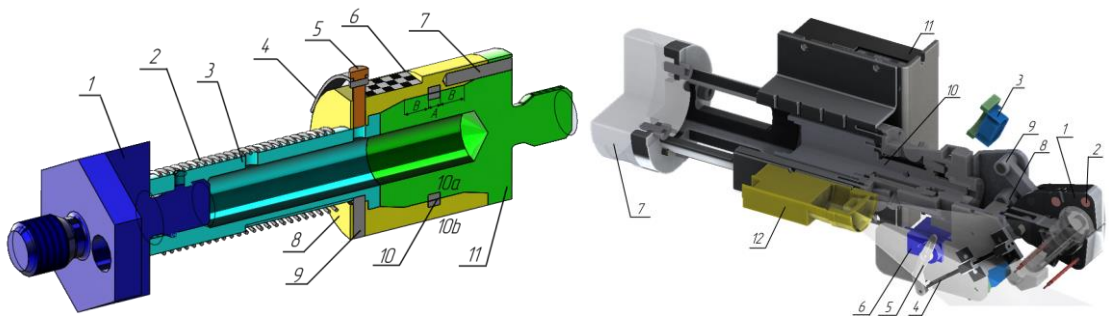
Базовая конструкция соединения ферменных конструкций и захват для сборки
